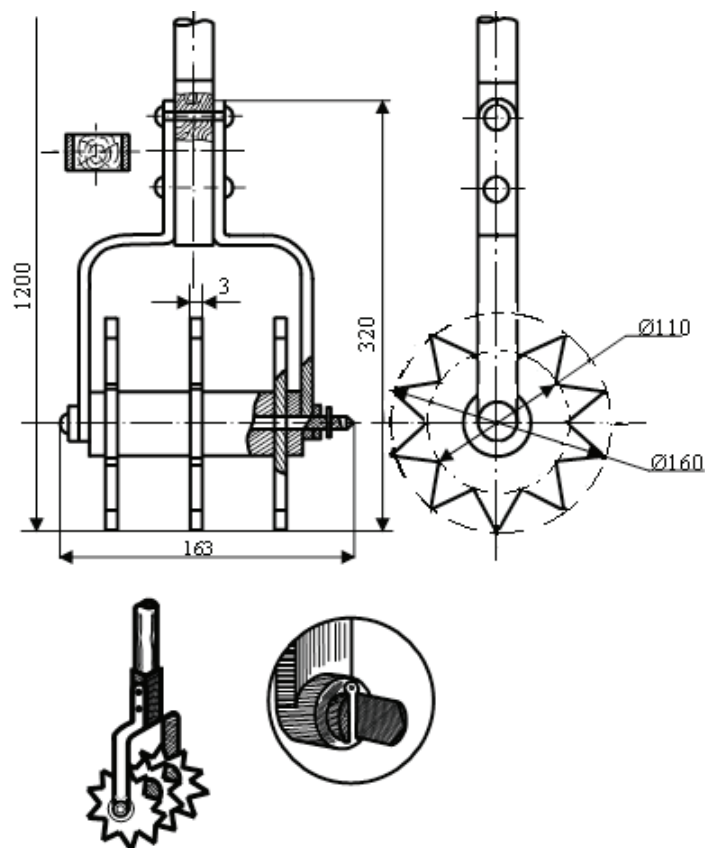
Чертеж зубчатки для рыхления почвенной корки
